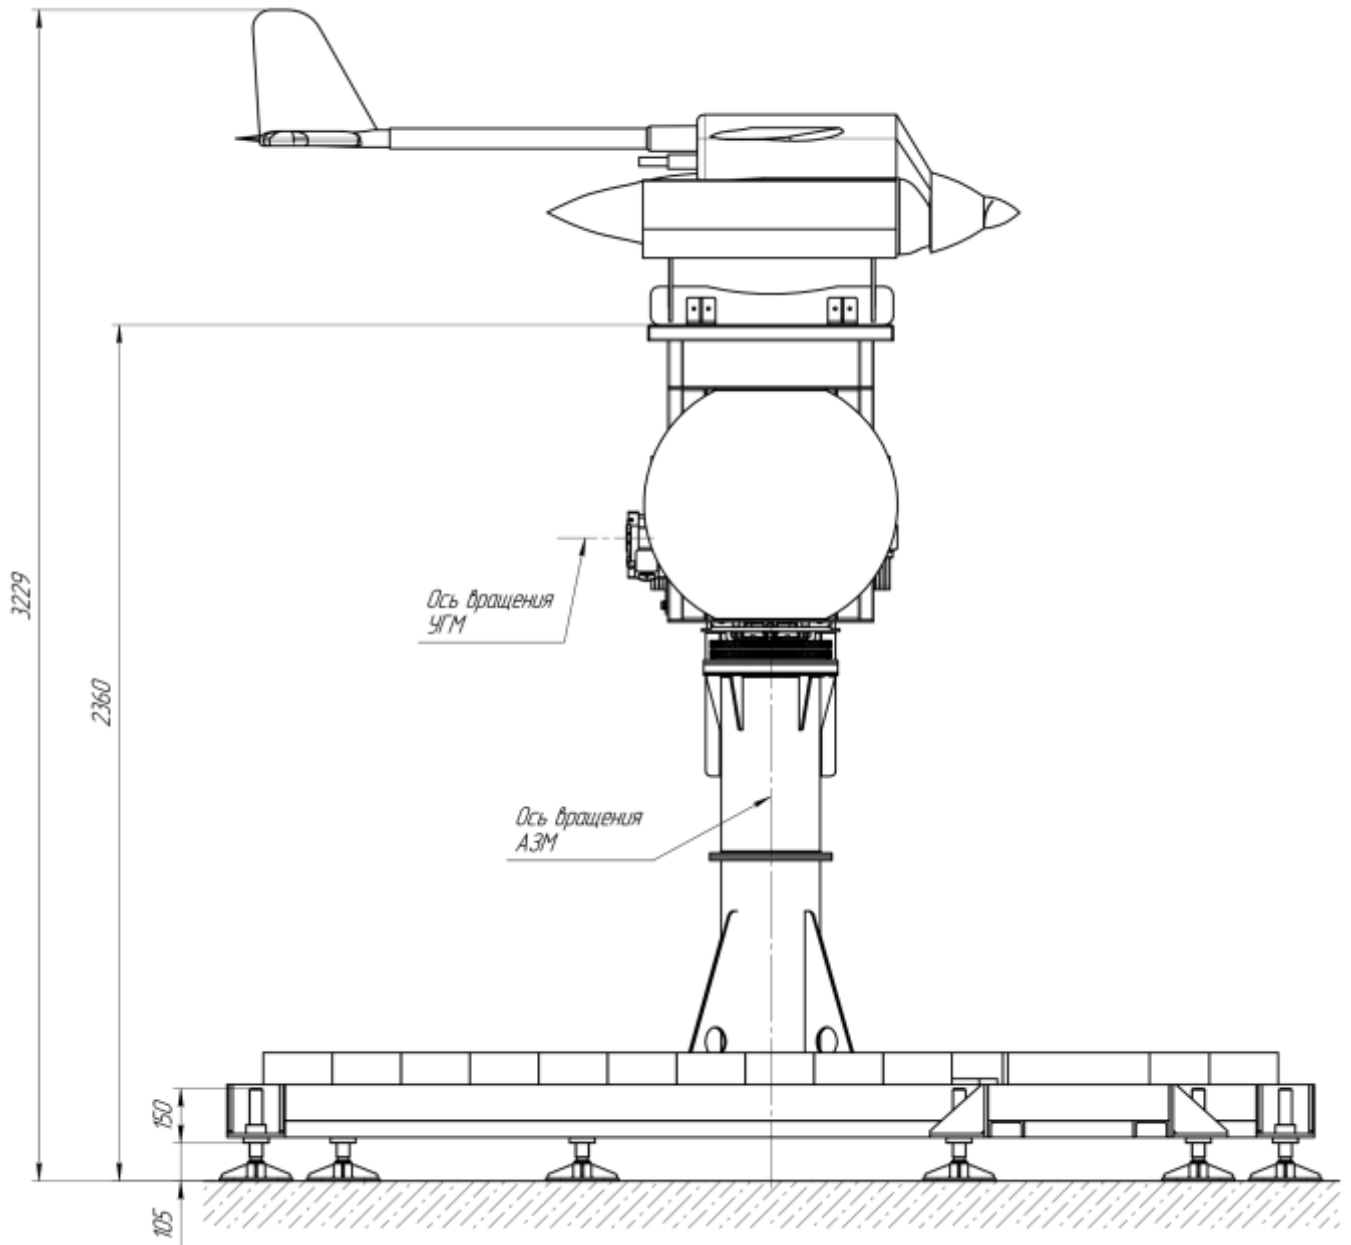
Габаритные размеры ОПУ СУ с размещаемым оборудованием Заказчика
